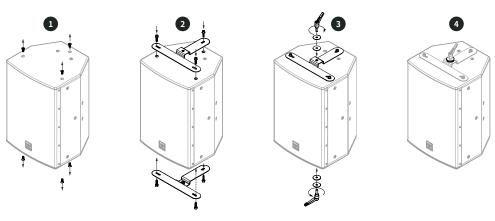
COX 12 MKII - Installazione con staffa di montaggio a parete.
